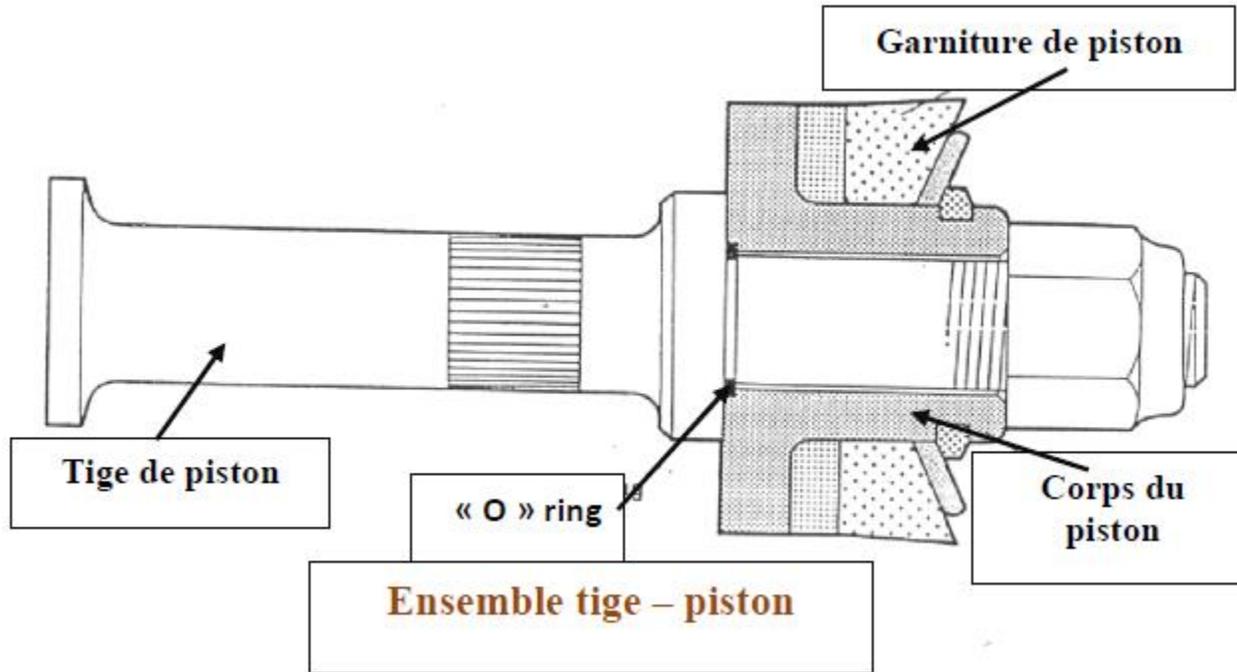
Le piston et la tige de piston d'une pompe à boue.
